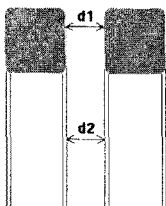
Welding 정밀도를 측정하기 위해 실행한 화면
